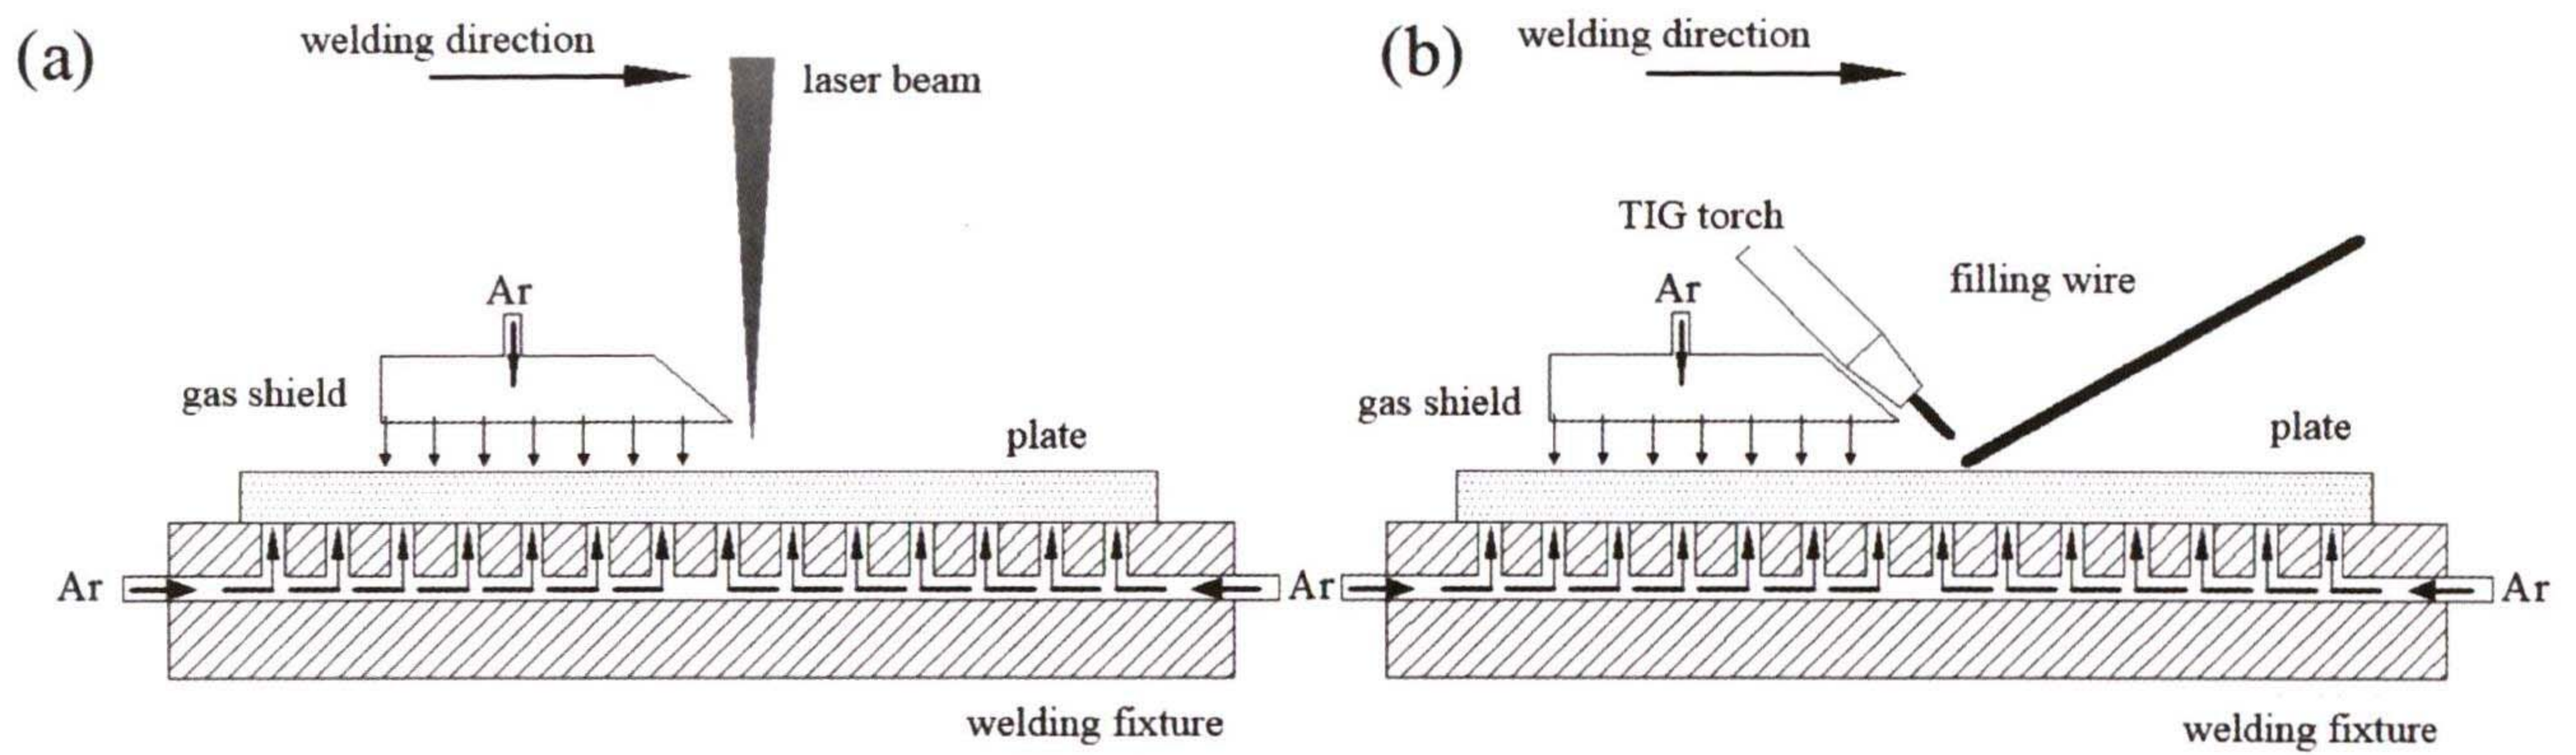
焊接试验装置示意图。(a)激光焊接；(b)TIG 焊接
